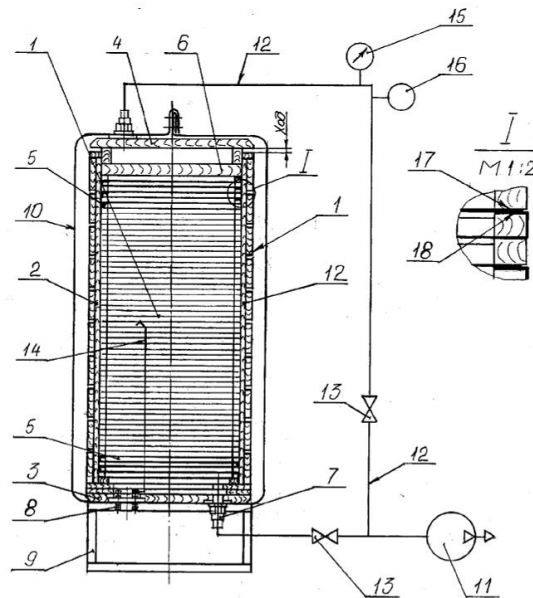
установка термовакуумной сушики: 1 – деревянный корпус; 2 – стенки корпуса; 3 – дно корпуса; 4, 6 – съемные крышки; 5 – лотки; 7 – вакуумный патрубок; 8 – токоотвод; 9 – подставка; 10 – вакуумная оболочка корпуса; 11 – вакуум-насос; 12 – вакуумный трубопровод; 13 – запорная арматура; 14, 15, 16 – системы контроля параметров сушики; 17, 18 – места электрического контакта между лотками
